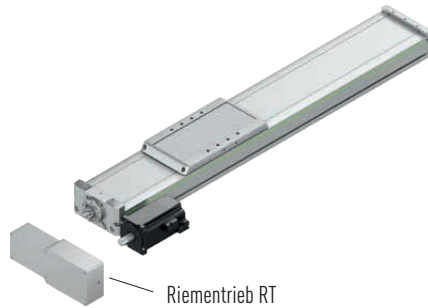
Motoradaption Linearmodule HM-S mit Riementrieb
